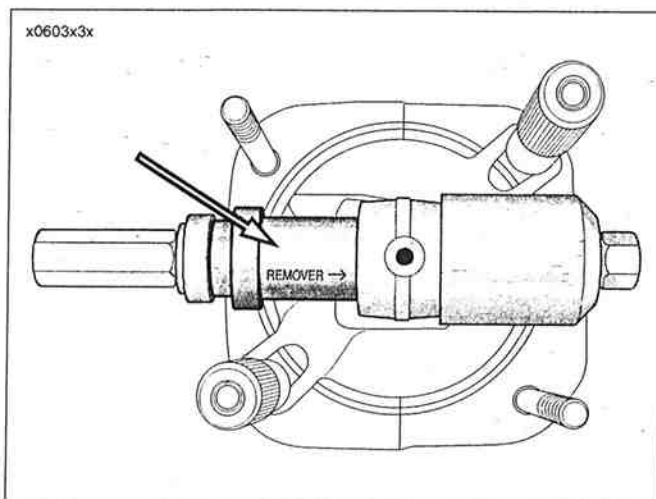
Disposición del extractor. Use el lado del extractor del extractor/instalador
